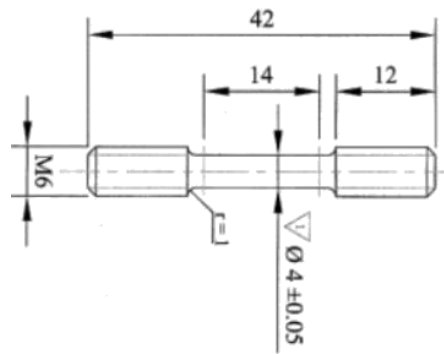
Dimensions (mm) des éprouvettes M6 utilisées pour les essais de traction.
